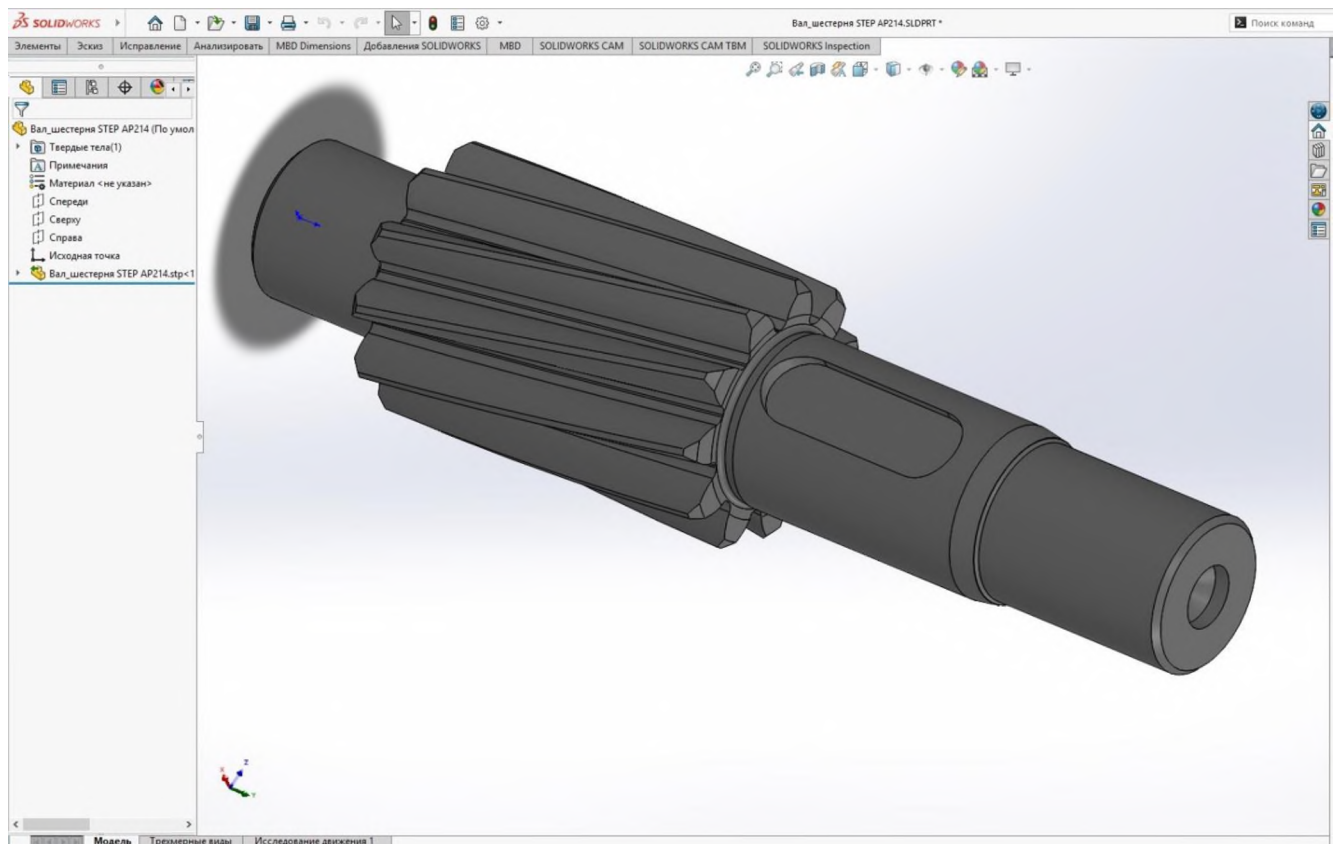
3D модель деталі «Вал-шестерня»
